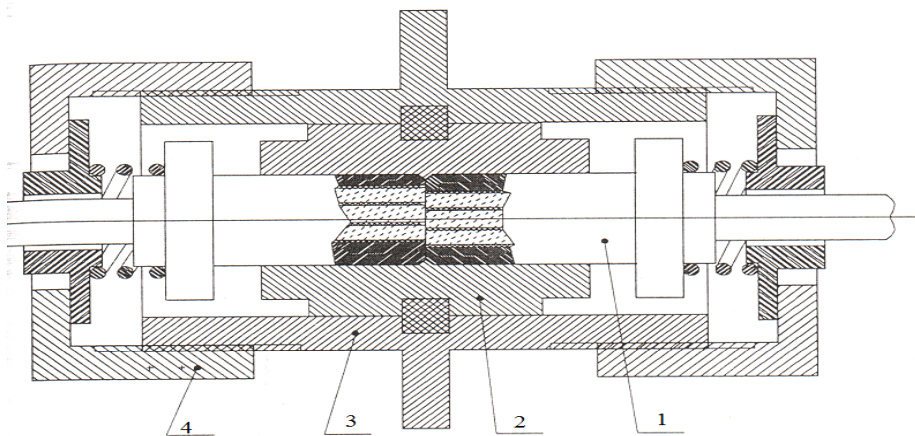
Схема конструкції роз'ємного багатомодового ОЗП
